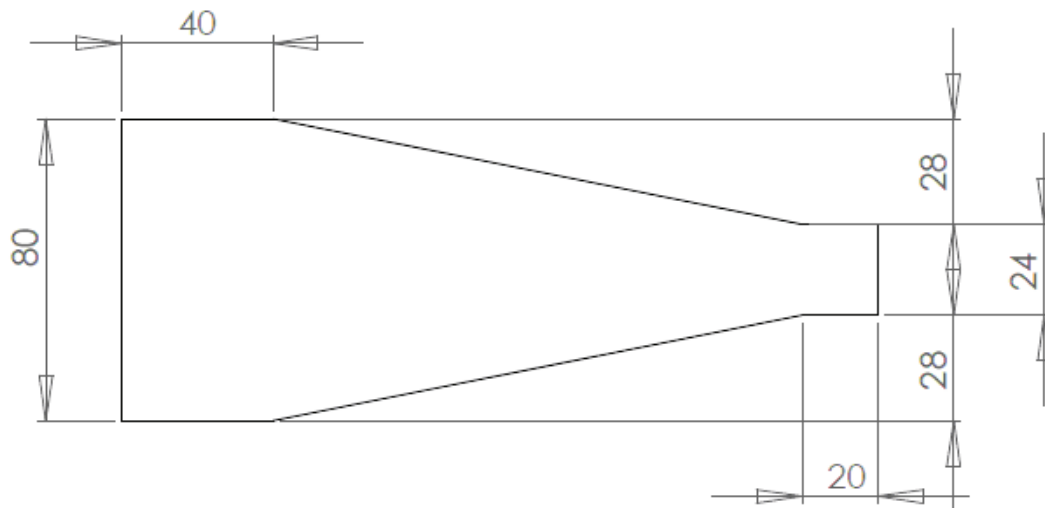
plan des éprouvettes trapézoïdales utilisées lors de la première campagne d'essais de fissuration à chaud, épaisseur 2 mm
